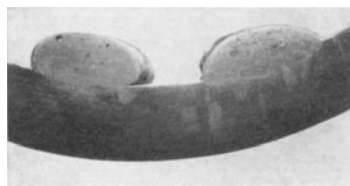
Querschnittsschliffe von aufgeschweißten Bronzeraupen ( $V = \frac{1}{2}$ ).
